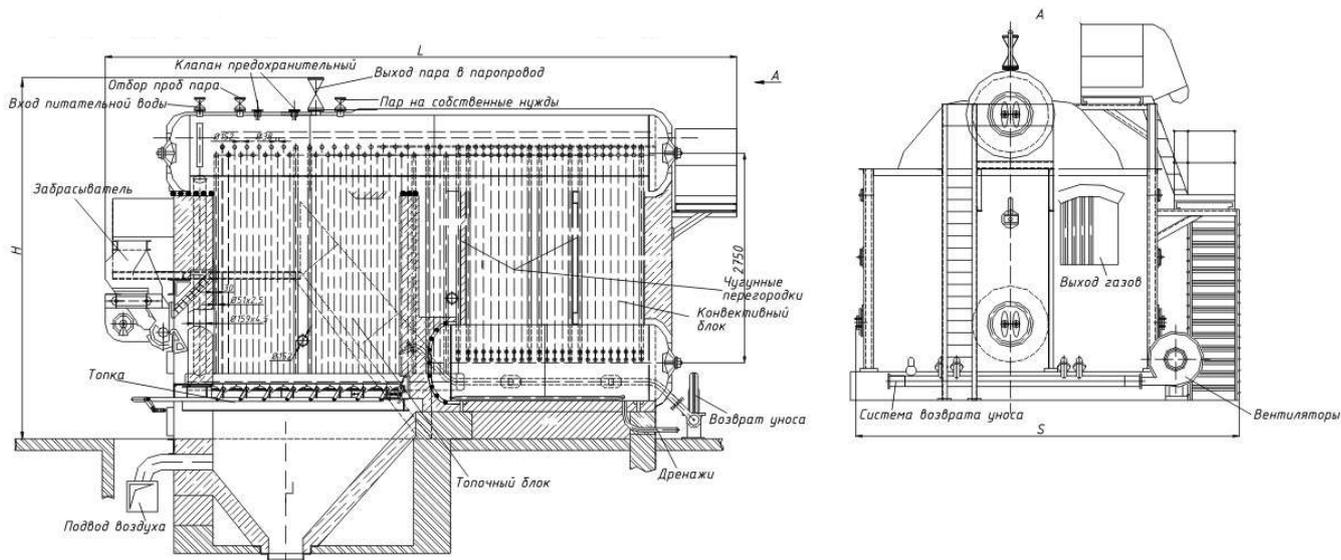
Устройство и габариты компоновки котла ДКВр-6,5/13
